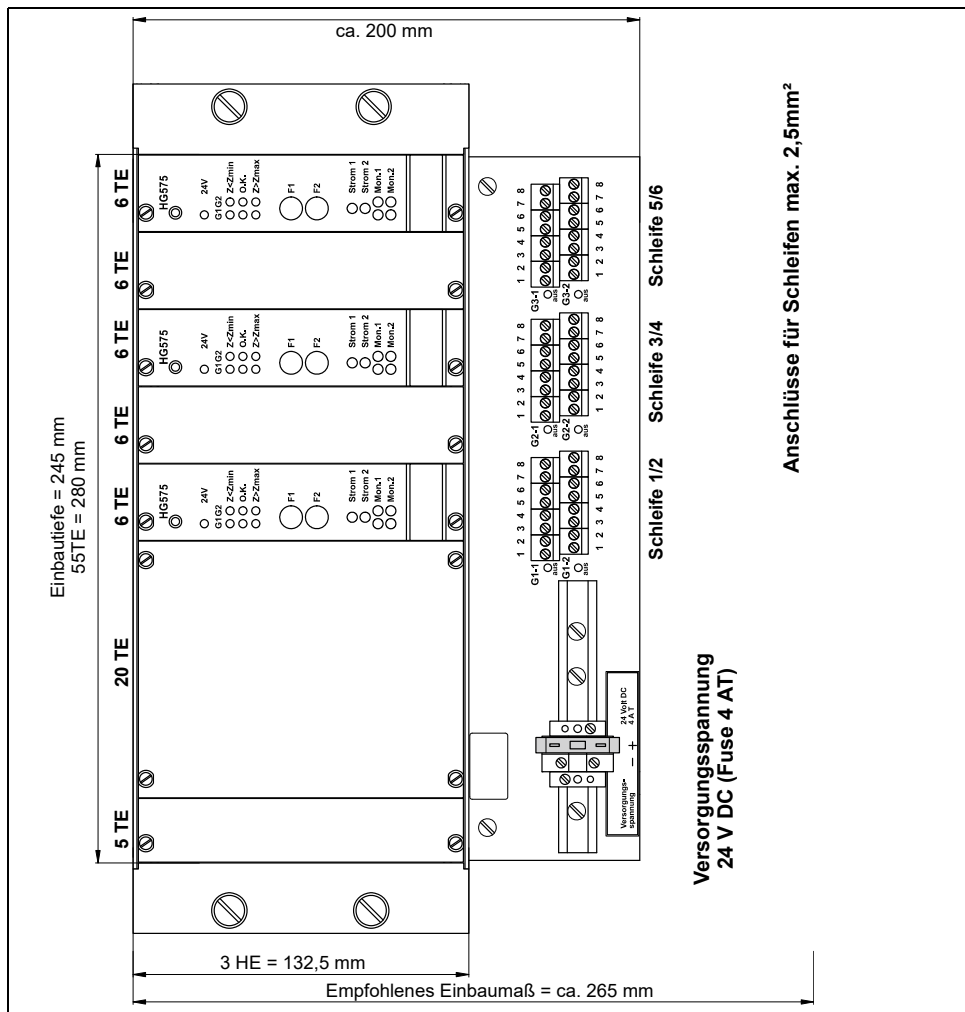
Zeichnung Gerätegruppenträger HG 93160-A mit Abmessungen
